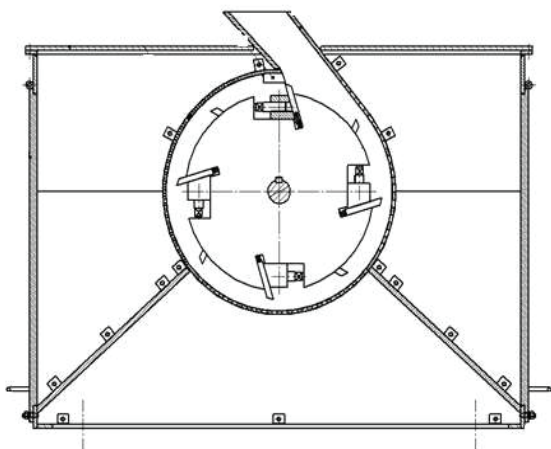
Общий вид роторно - ножевой мельницы МР – 4
